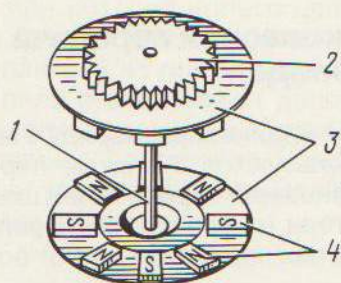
Ротор шагового двигателя со встроенными катушками:
